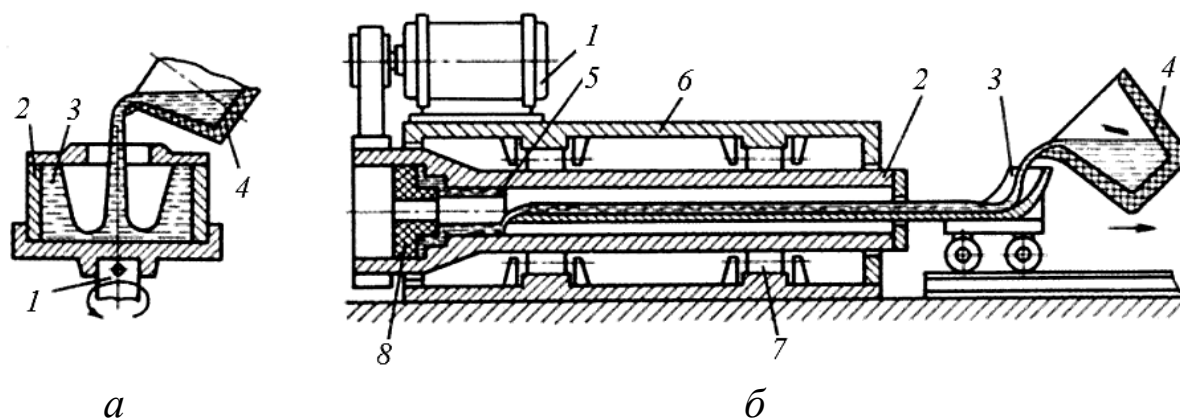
Схемы процессов изготовления отливок центробежным литьем
